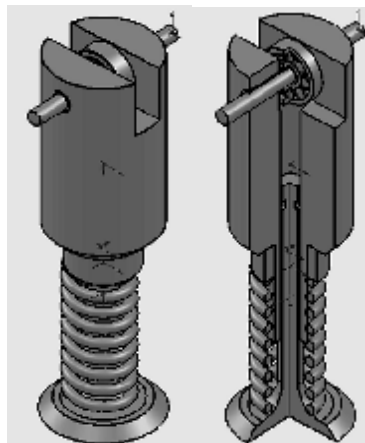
Рабочая часть установки с экспериментальными образцами
